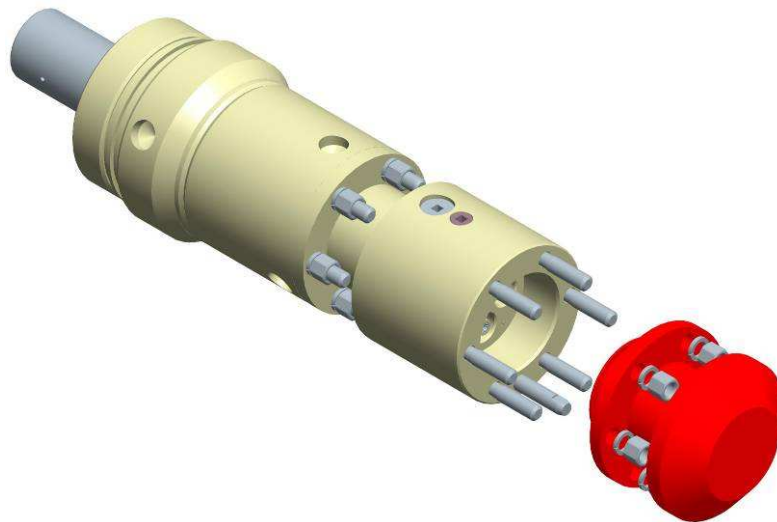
Внешний вид опоры подшипника ОП-103А
